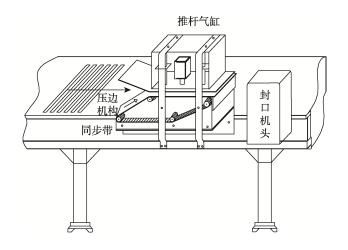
带压边机构的缝纫封口系统 Fig.3 Sewing and sealing system with edge pressing mechanism
